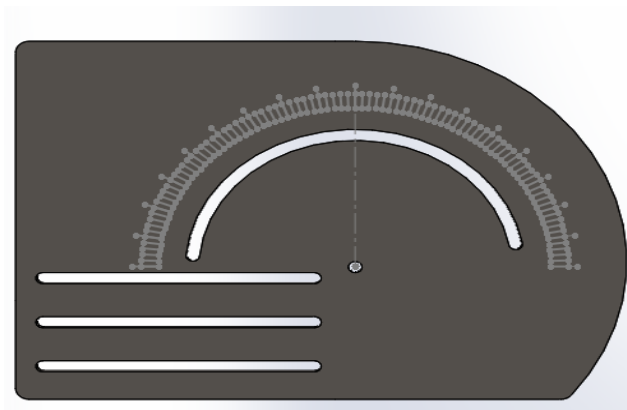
Desenho CAD de Mordente móvel de morsa para a fixação de tubos
